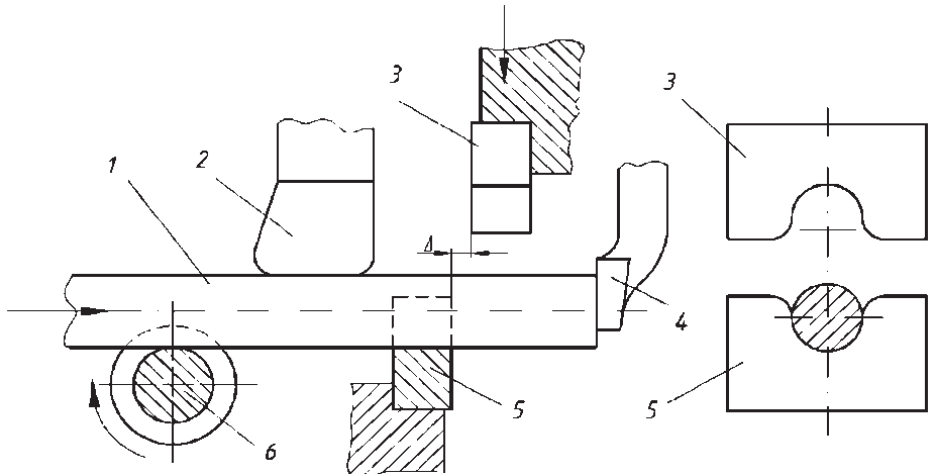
Схема резки сортового проката на пресс-ножницах: 1 – заготовка; 2 – прижим; 3 – подвижный нож; 4 – регулируемый упор; 5 – неподвижный нож; 6 – рольганг
